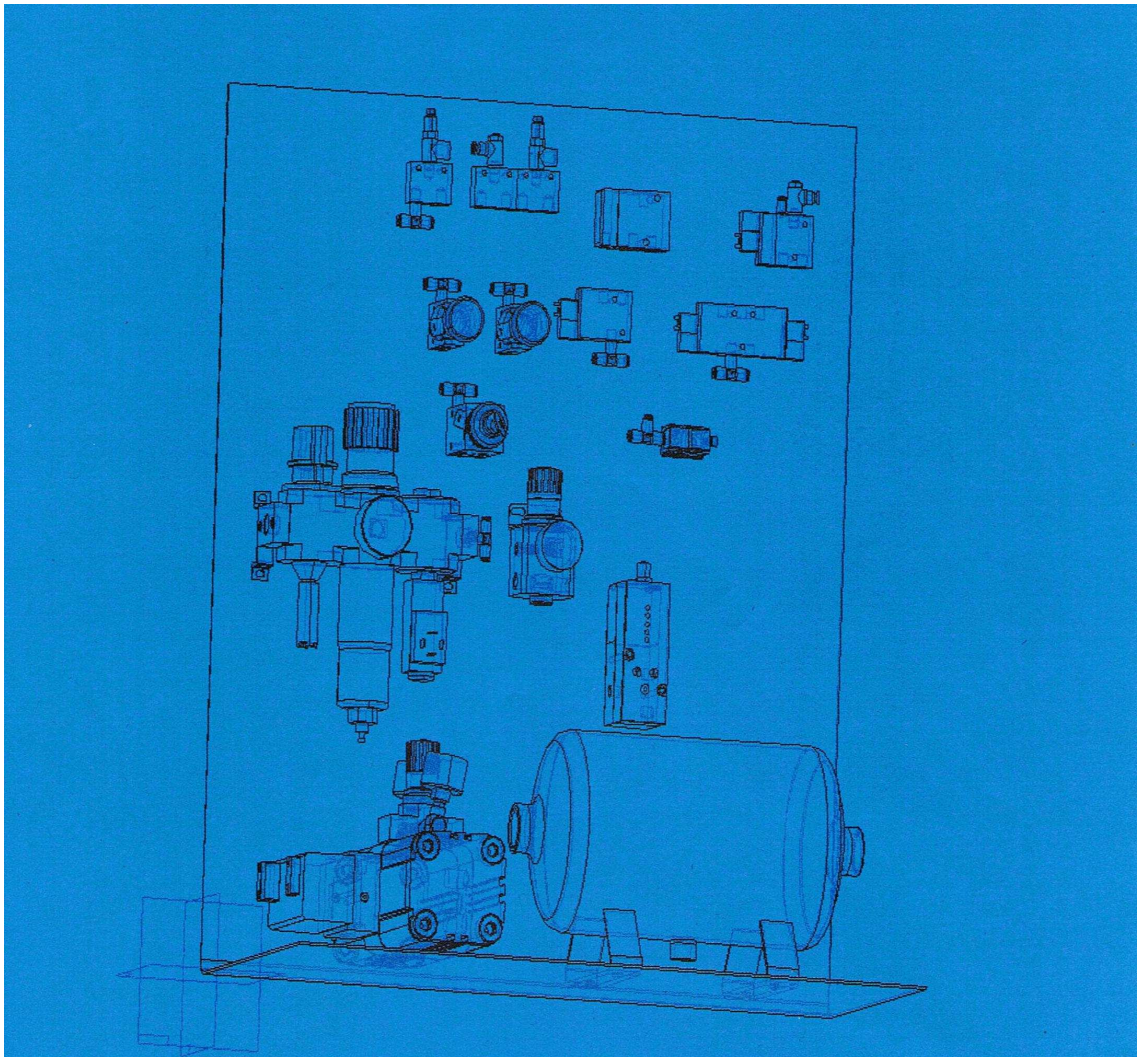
Zeigt die Entwurfsanordnung der pneumatischen Komponenten auf der Montageplatte
